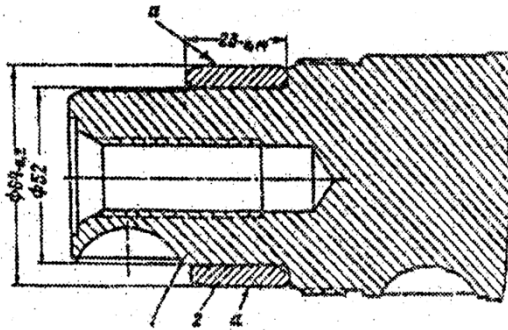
Установка ремонтной втулки под переднюю манжету коленчатого вала:
